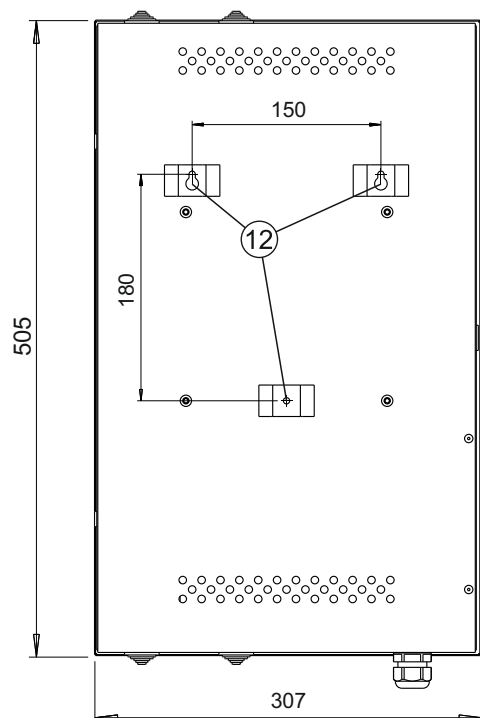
Внешний вид, габаритные и установочные размеры бокса
